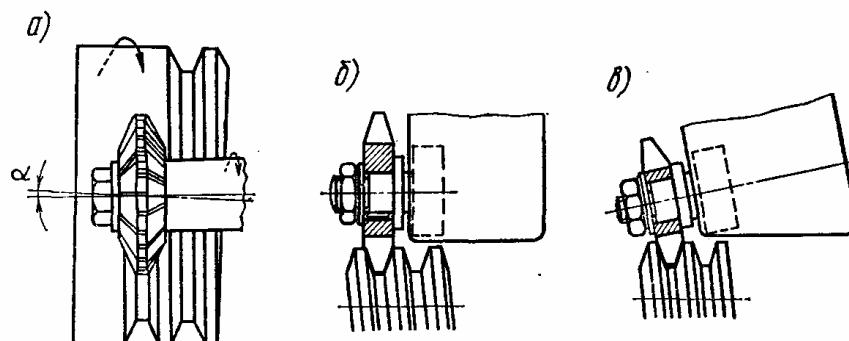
Схемы фрезерования резьбы дисковыми фрезами:
